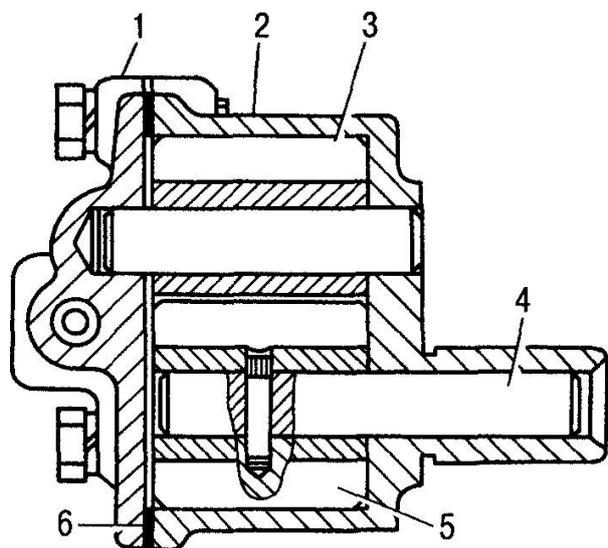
Масляный насос: 1 - крышка; 2 - корпус; 3 - ведомая шестерня; 4 - валик; 5 - ведущая шестерня; 6 - прокладка
